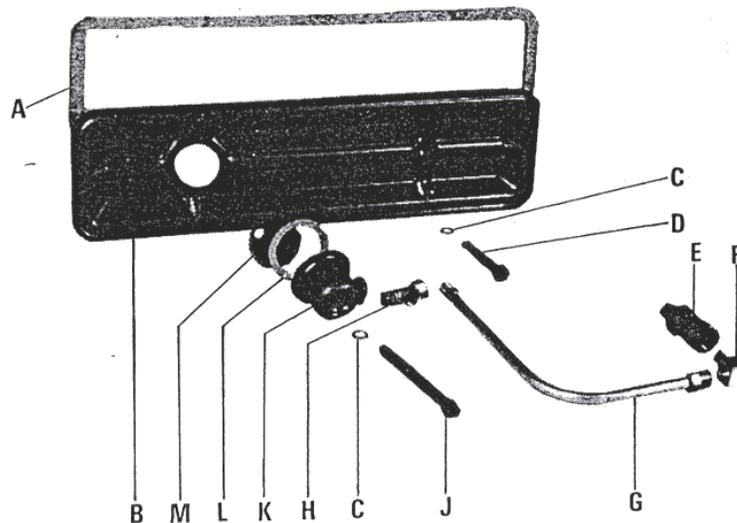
Plaque de visite des ressorts de soupapes; vue éclatée
